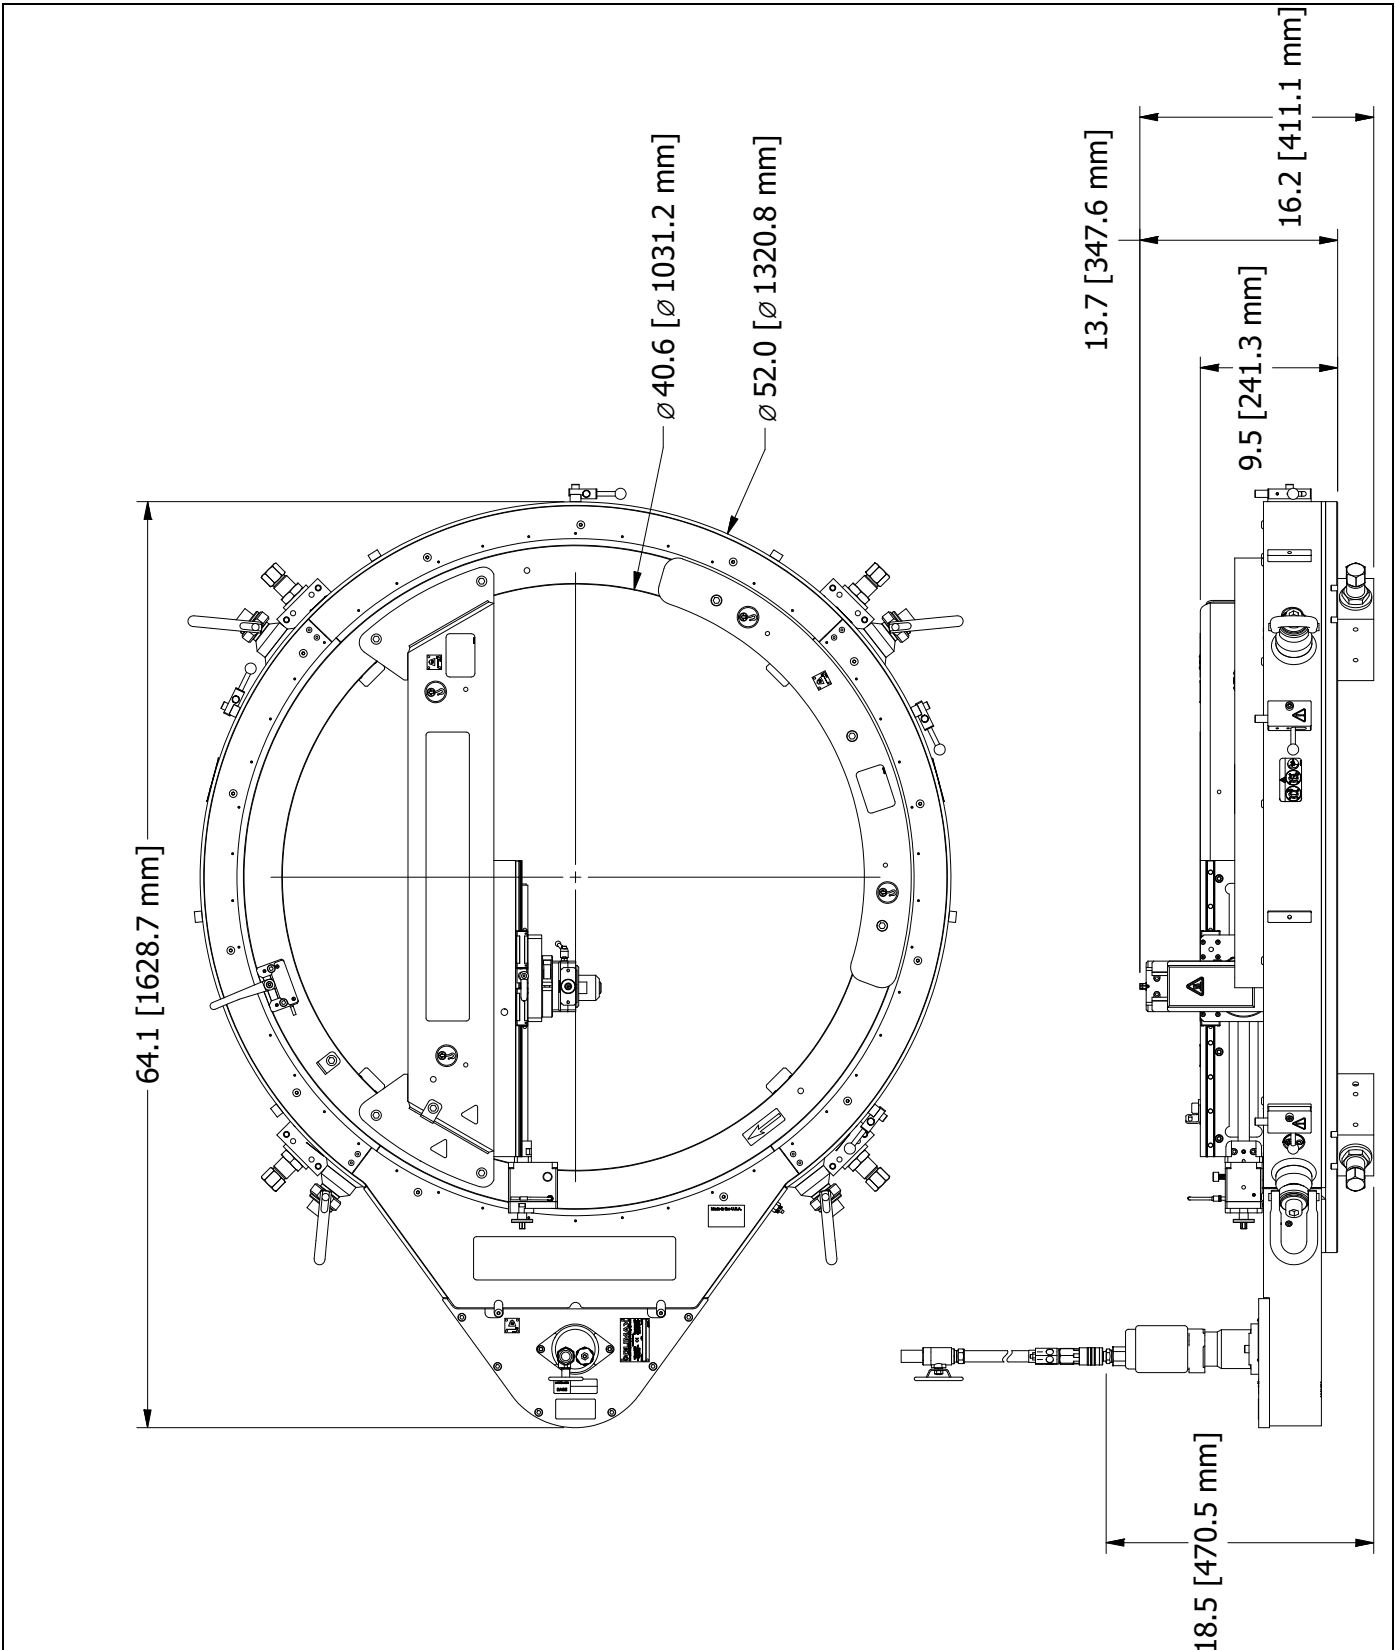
DIMENSIONES DE LA ODF40 SPEED FACER (N/P 86870)
